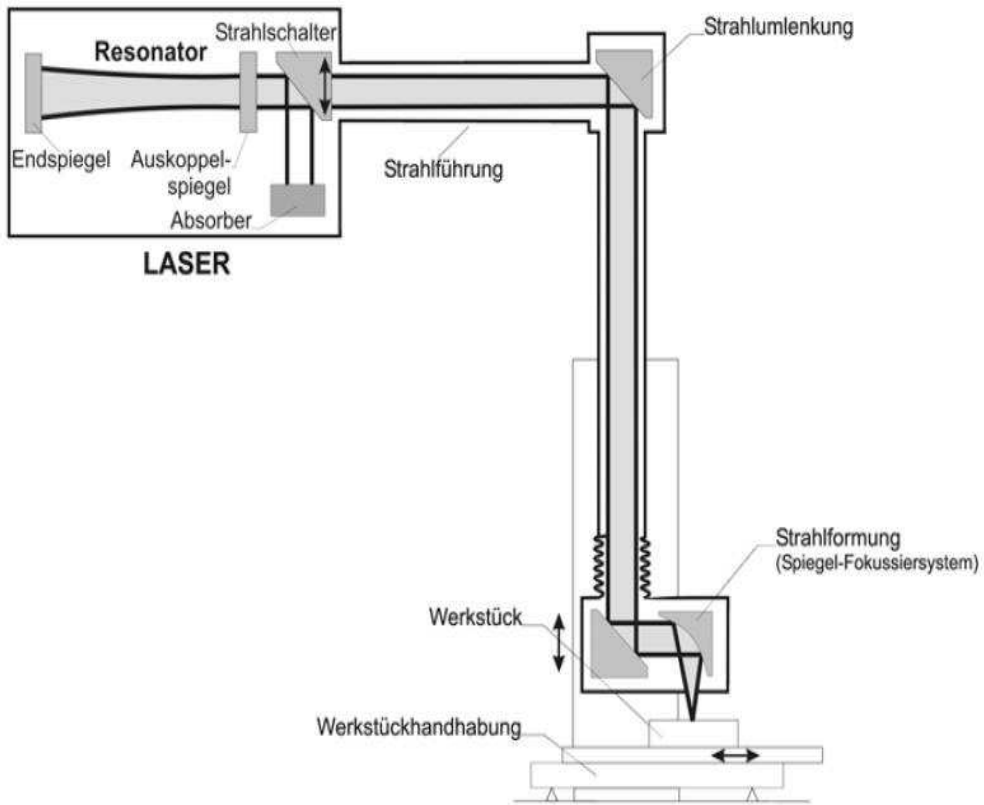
Prinzipieller Aufbau einer Laserschweißanlage<sup>[ST01]</sup>
